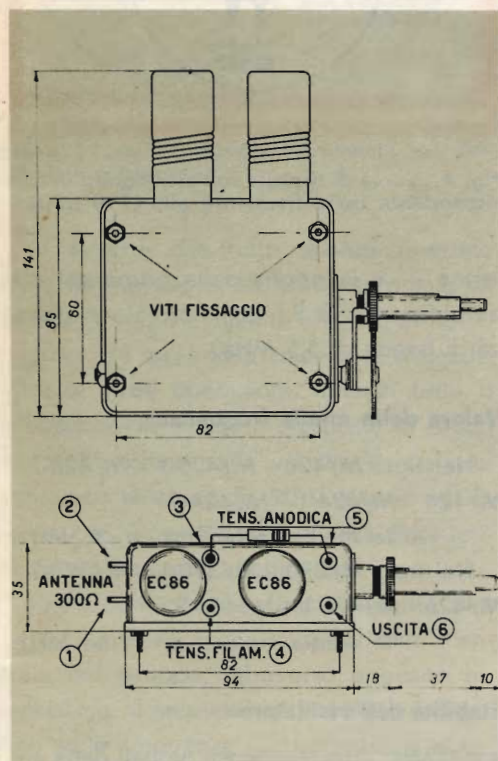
Dimensioni d'ingombro del gruppo U.H.F. M/390.
